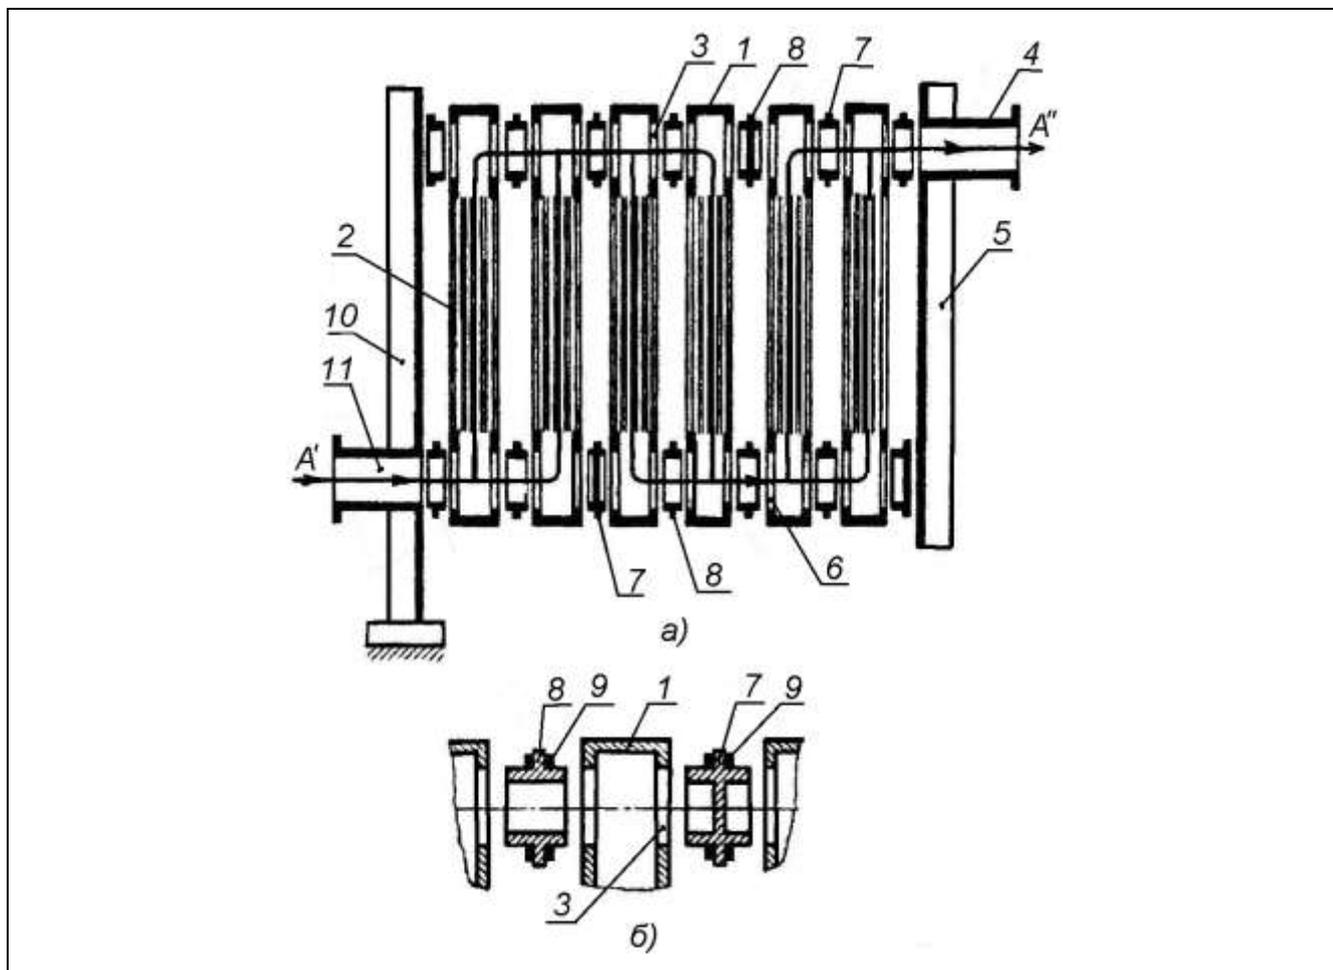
Блочный сварной пластинчатый теплообменник марки ТПБС: *а)* – общий вид; *б)* – схема расположения проходных 8 и глухих 7 втулок с уплотнительными прокладками 9
